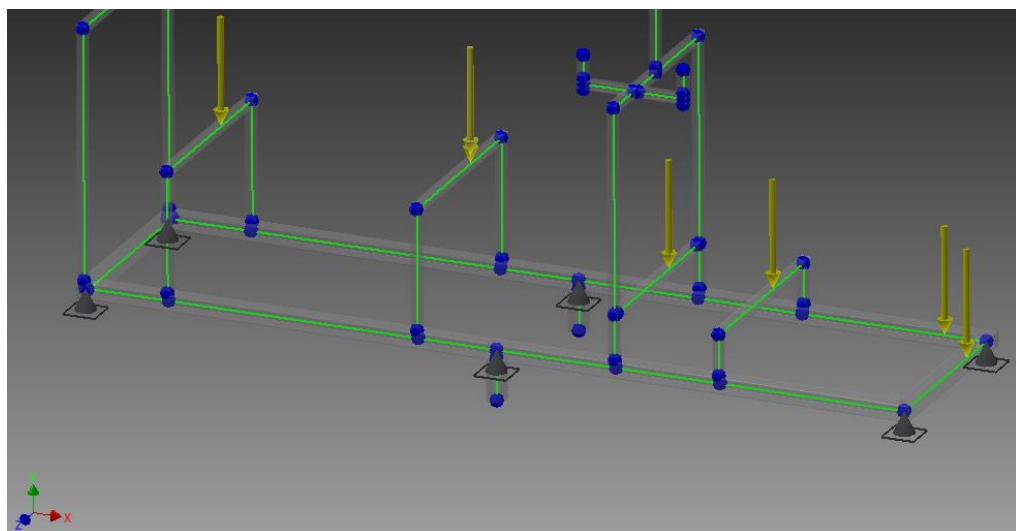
Apoyos en la estructura donde va soportado el equipo. Fuente: Autor
